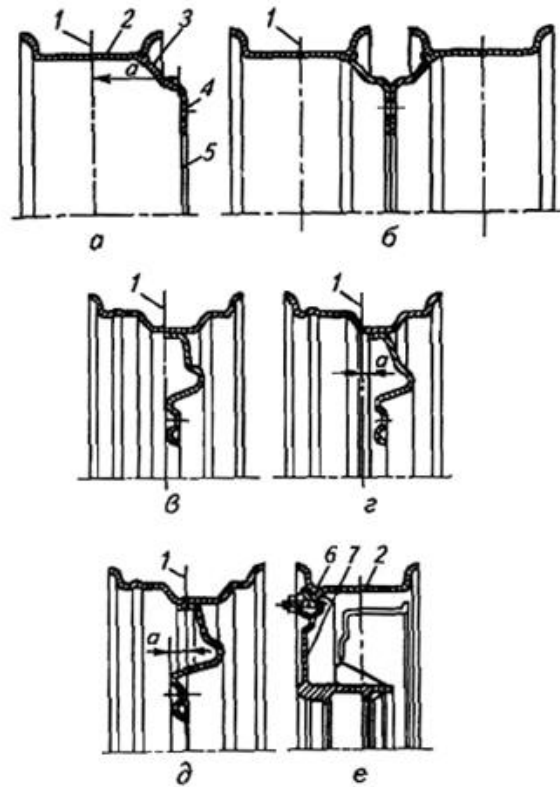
Конструктивные схемы колес: а - одинарного; б - двойного; в, г, д - с различными вылетами диска; е - бездискового; 1 - вертикальная ось колеса; 2 - обод; 3 - диск; 4 - крепежные отверстия; 5 - центральное отверстие диска; б - элементы крепления; 7 - ступица
